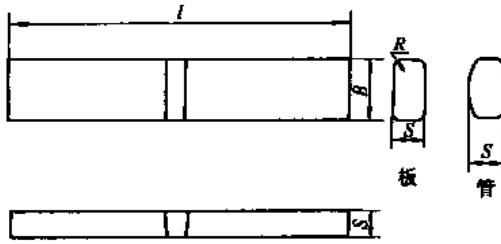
焊接接头纵向面弯试样形状和尺寸
